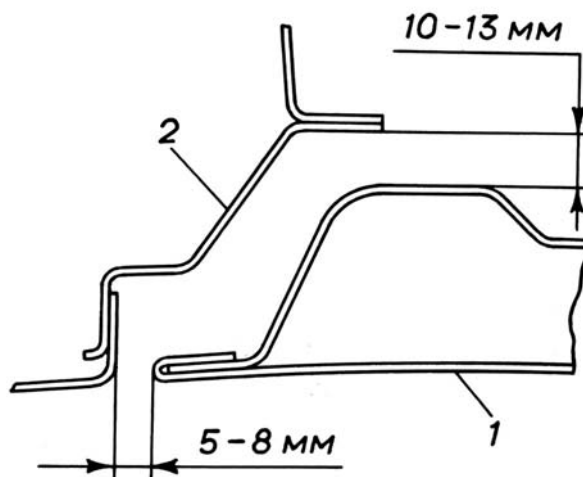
Установка боковой двери: 1 - дверь; 2 – боковина
